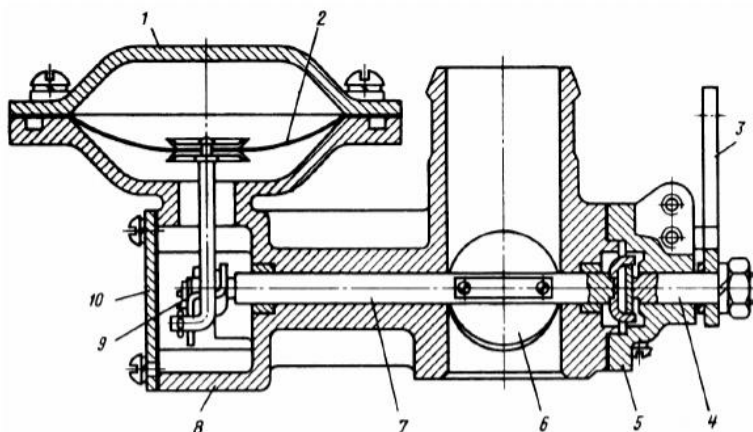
Дозатор газа газодизельных автомобилей семейства КамАЗ: 1 - крышка ограничителя оборотов; 2 - диафрагма ограничителя оборотов; 3 - рычаг привода
